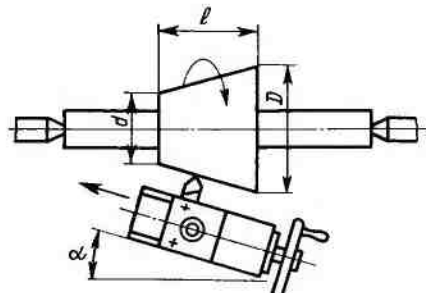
Обработка конуса поворотом резцовых салазок
